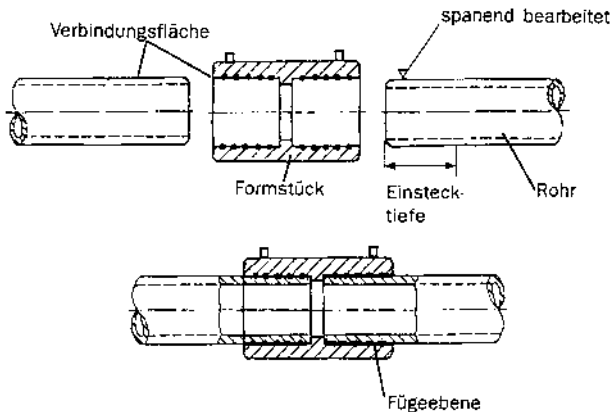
Heizwendelschweißen einer Muffe (Prinzip).
